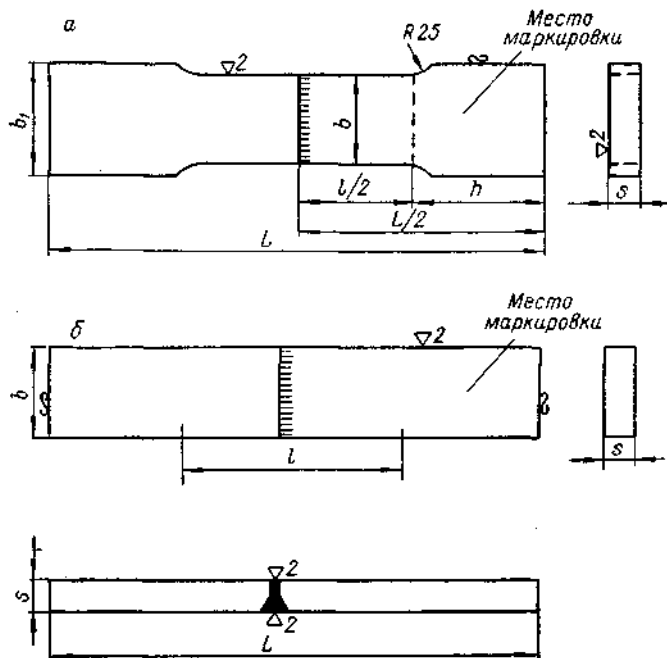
Образцы для механических испытаний качества варки: а — на разрыв, б — на изгиб.
